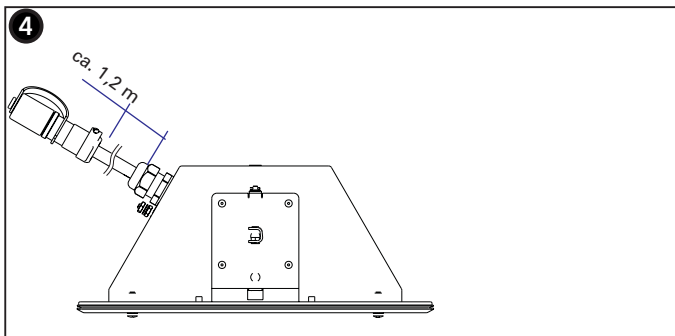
Montagegehäuse eBB 12 NE mit Anschlusskabel GHG 571
